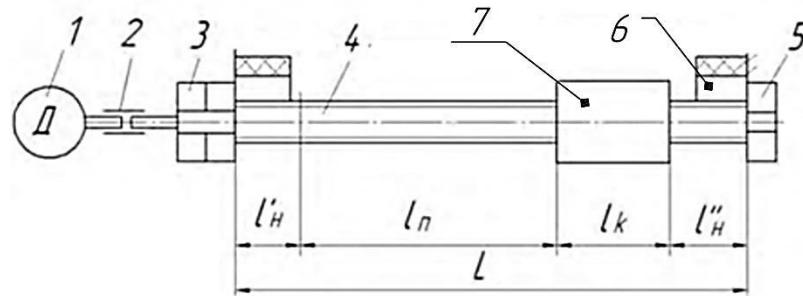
Схема до визначення довжини гвинта: 1—двигун; 2—муфта; 3, 5—опори гвинта; 4—гвинт; 6—корпус для встановлення КПП; 7—гайка
